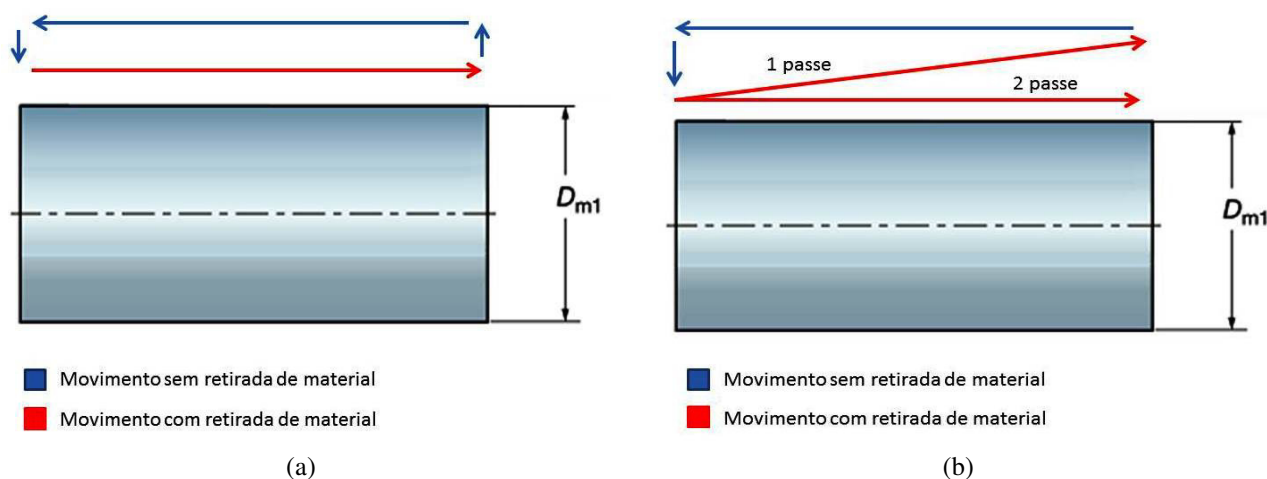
Estratégias de usinagem. (a) Corte longitudinal. (b) Corte cônico ou em rampa.
